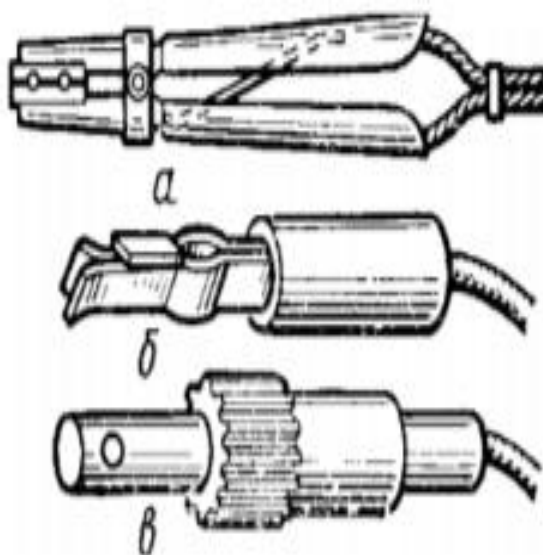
Електротримачі для ручного дугового зварювання:
